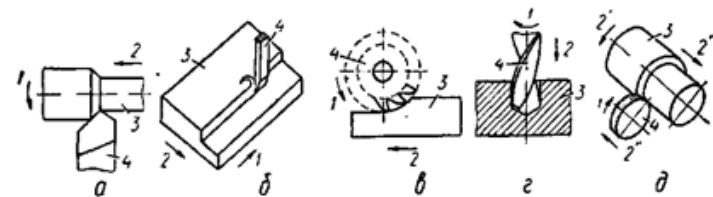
Типові способи обробки металів на металорежущих станках
